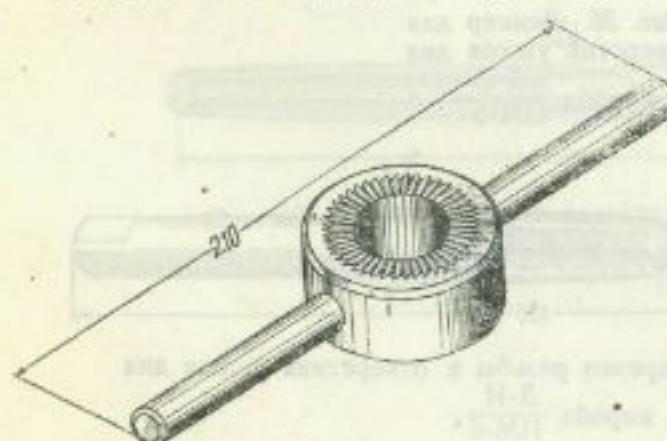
Шарошка для бронзовой гайки ствола Д-И ПМ-1.
